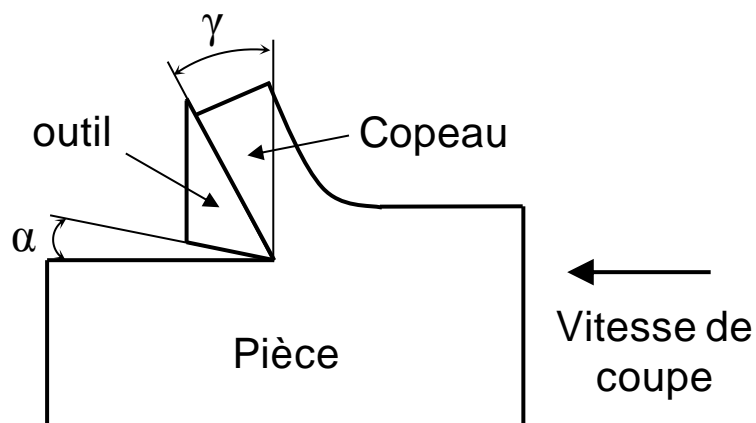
Définition des angles d'outil principaux en coupe orthogonale.
